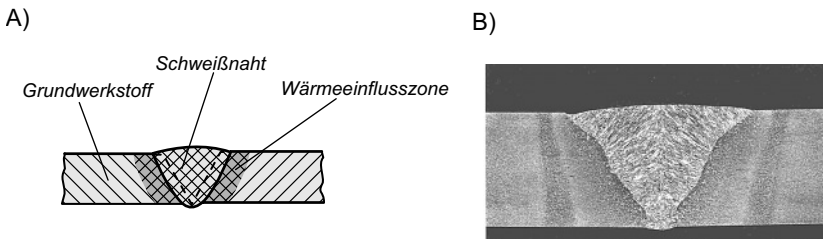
Schmelzschweißverbindung; A) Schematisch, B) Real, lichtmakroskopisch
